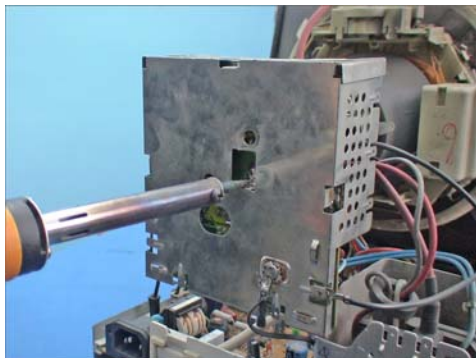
焊掉显像管管座焊点上的焊锡
